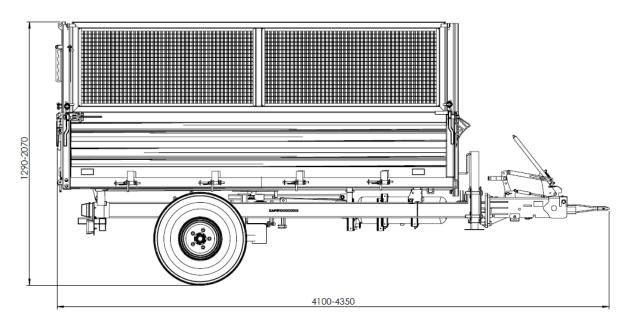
Габаритные размеры прицепа с инерционным тормозом – вид сбоку
